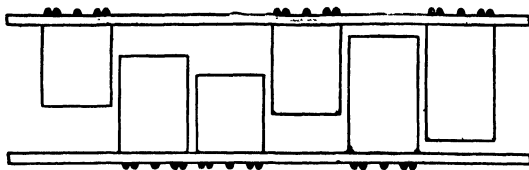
Двухплатная конструкция блока с чередующимся расположением микромодулей.
